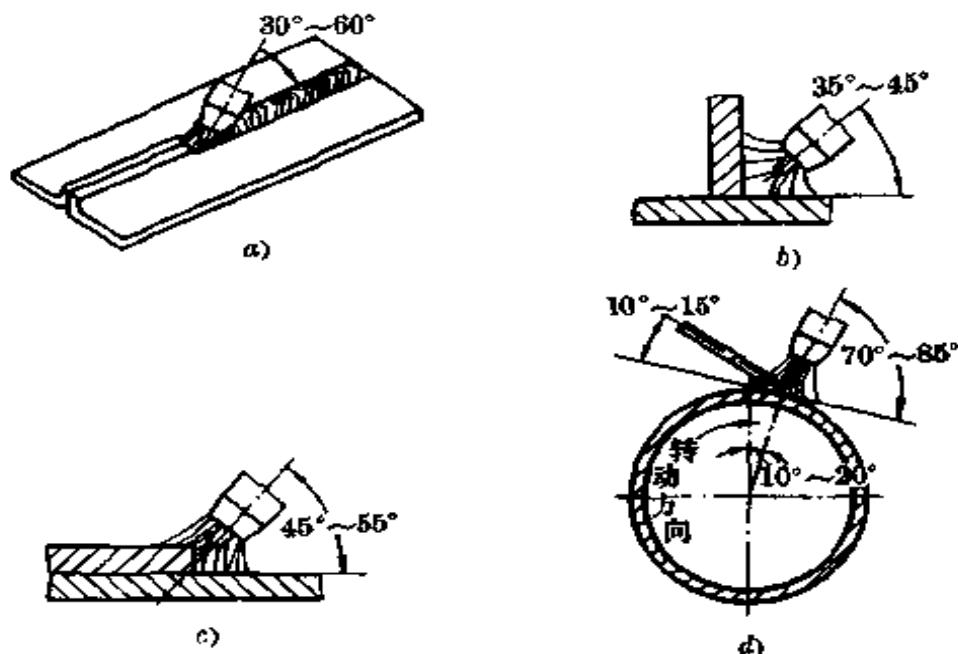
常见接头形式平焊时焊枪或焊丝与工件的相对位置
